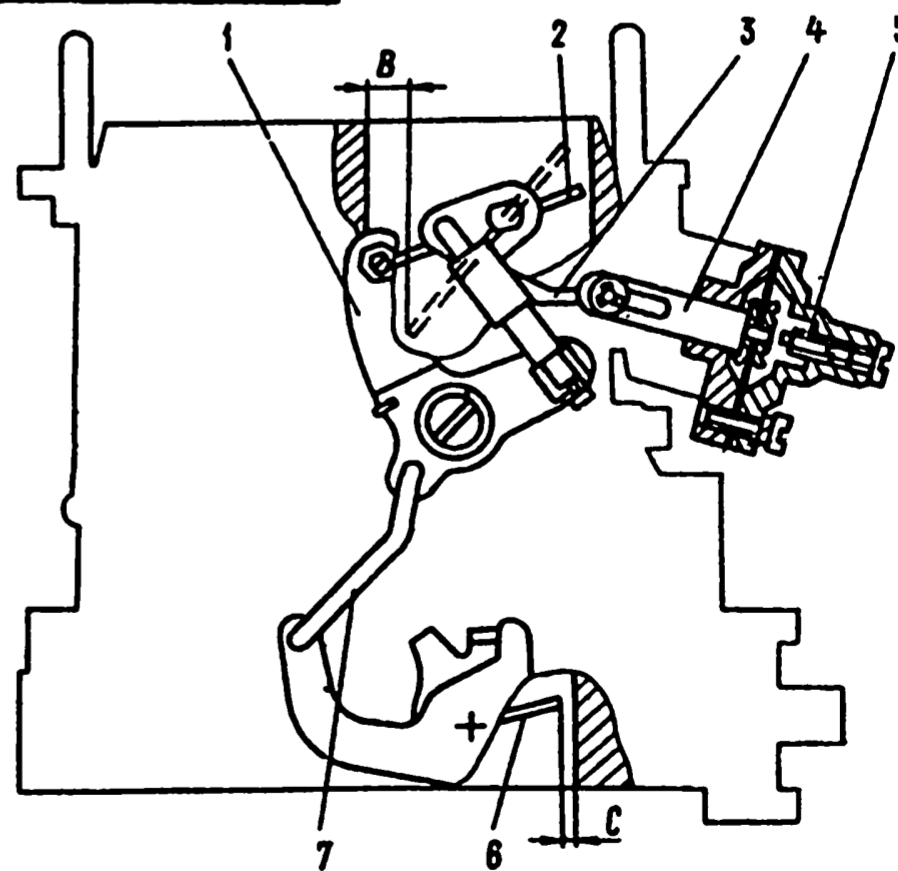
Регулировка привода пускового устройства карбюратора 2105-1107010: 1 - трехплечий рычаг привода воздушной заслонки; 2 - воздушная заслонка; 3 - тяга пускового устройства; 4 - шток; 5 - регулировочный винт; 6 - дроссельная заслонка первой камеры; 7 - тяга привода дроссельной заслонки
